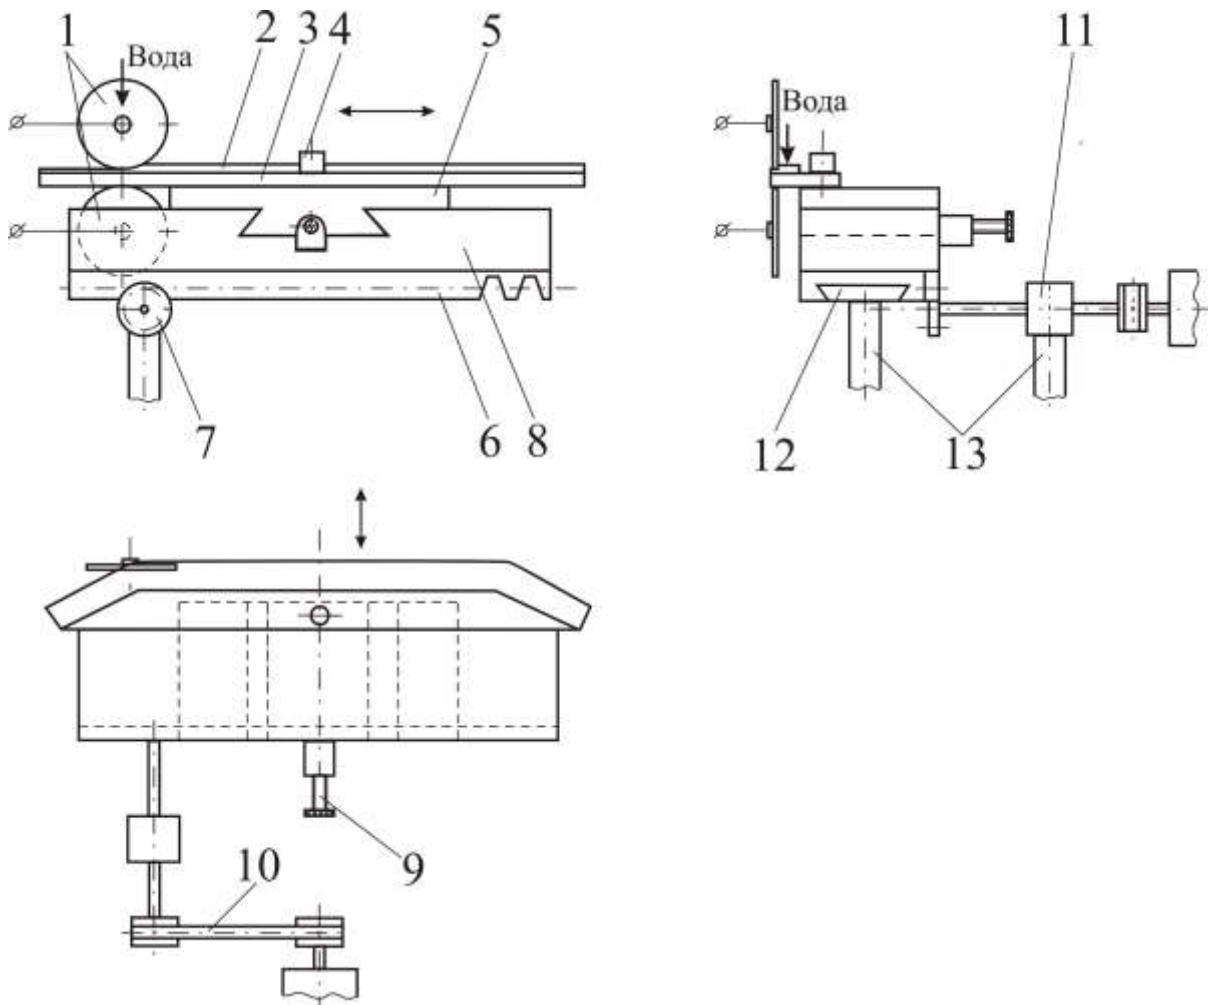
Схема пристосування для контактного наварювання полозів: 1 – роликові електроди; 2 – кераміко-металева композиційна стрічка; 3 – полоз; 4 – штифт; 5 – верхній повзун; 6 – рейка; 7 – шестерня; 8 – нижній повзун; 9 – передача гвинт-гайка; 10 – пасова передача; 11 – підшипникова опора; 12 - направляюча платформа; 13 – опори
